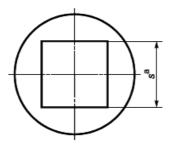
Калибр для проверки допуска формы, установленного на рисунке 25
